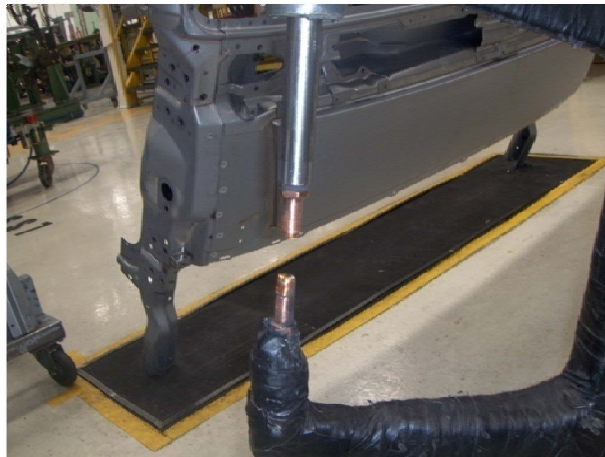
PINÇA DE SOLDADURA SELECIONADA PARA O ESTUDO
